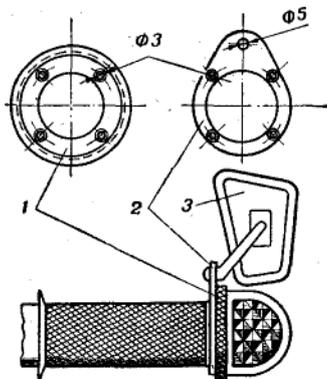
Крепление зеркала на руле мотороллера «Вятка» и В-150 М
